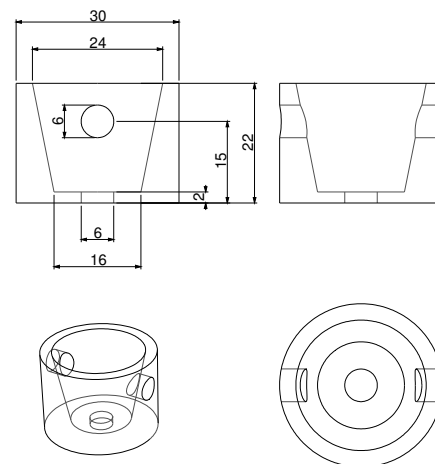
Disegno meccanico del bugliolo, dimensioni in millimetri
